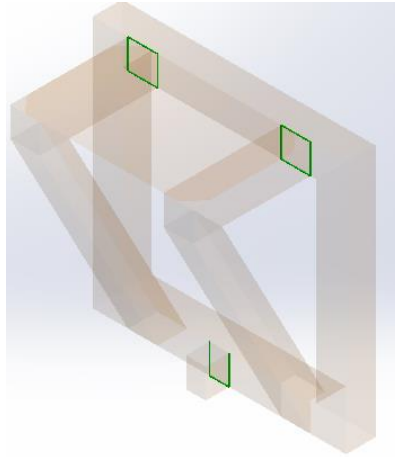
Cordones de soldadura críticos en la parte móvil.
